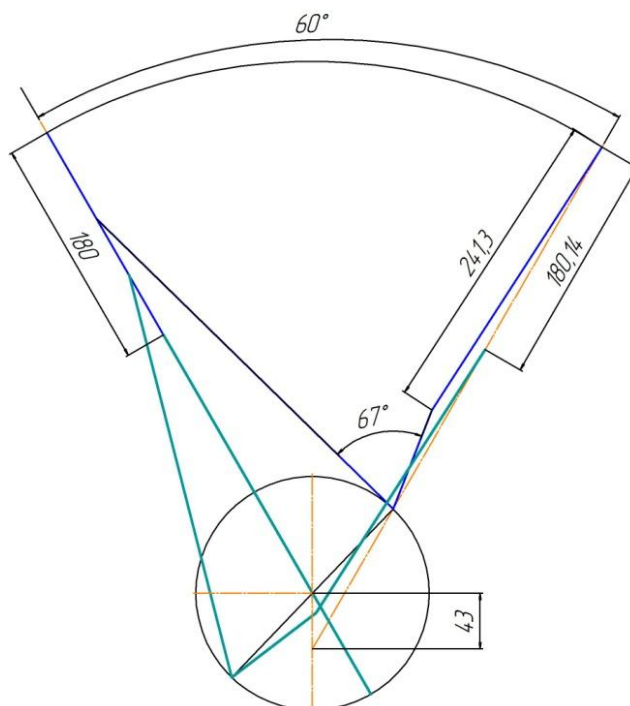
Кинематическая схема формирования одинакового хода поршней при смещении одной оси цилиндра двигателя
